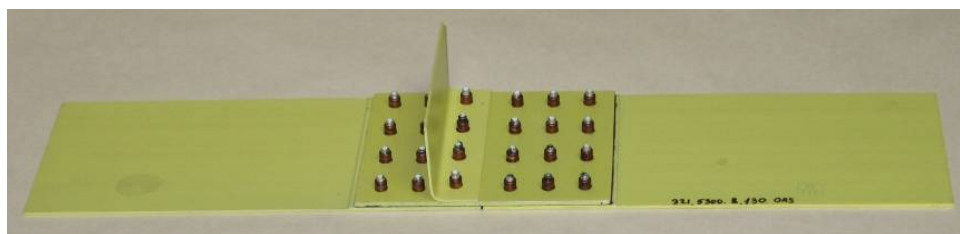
Образец поперечного стыка фюзеляжа на болт-заклепках
